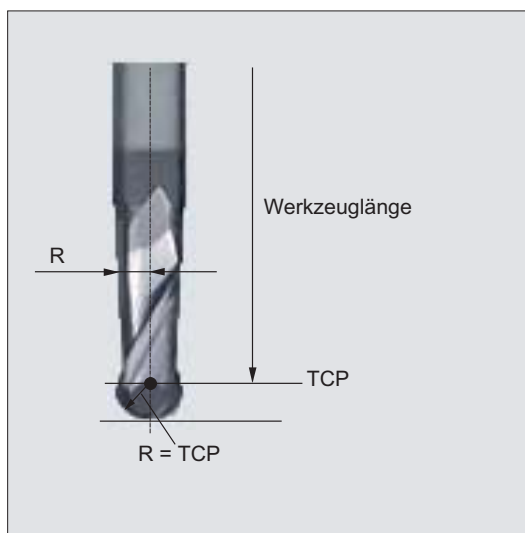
Als Werkzeuglänge des Radienfräsers muss die Länge bis zum TCP (Tool Center Point) eingegeben werden.
